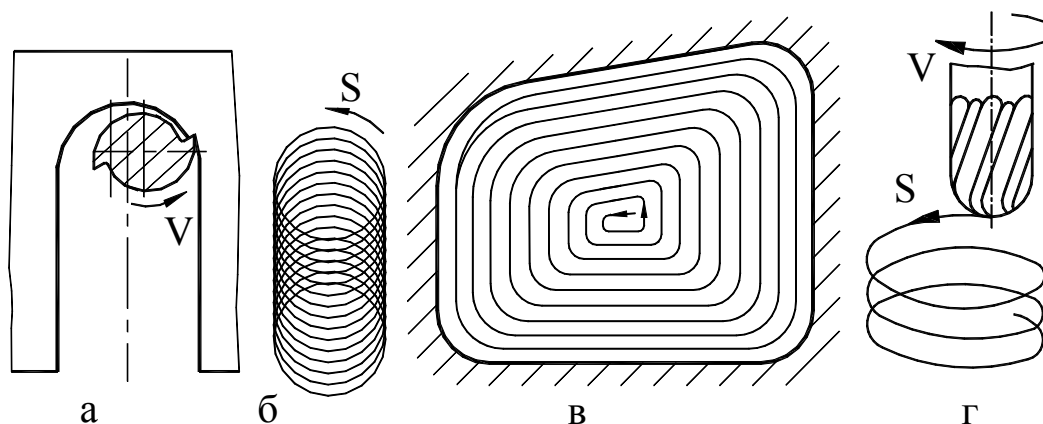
Траектория движения фрезы при ВСО: а – обработка паза; б – траектория движения фрезы при обработке паза; в – траектория движения фрезы при обработке колодца; г – расфрезеровывание отверстий
